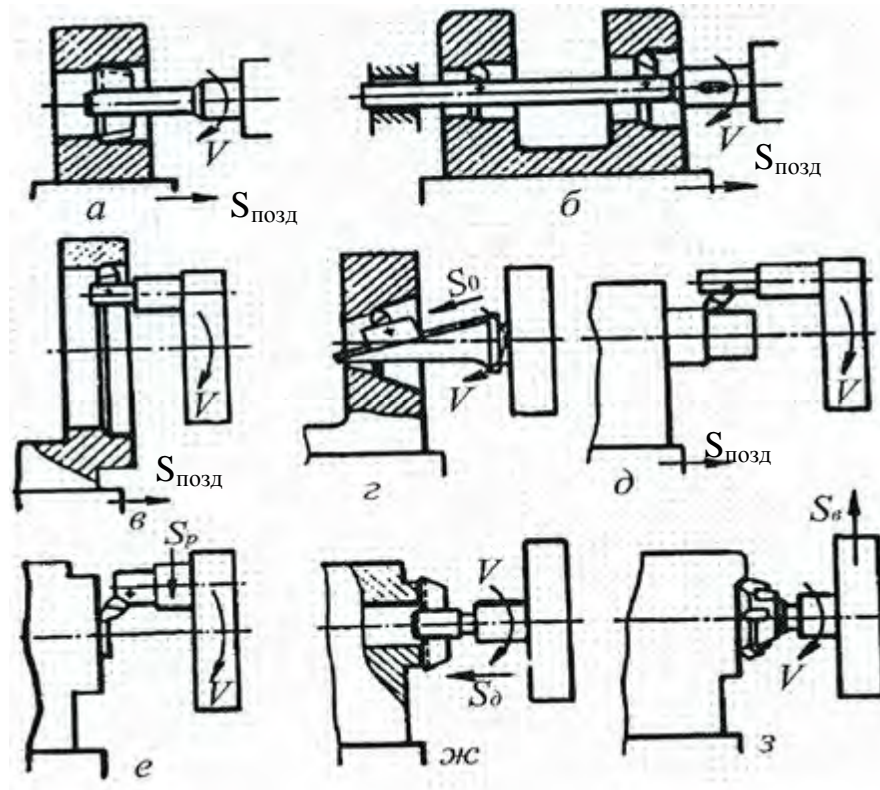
Схеми оброблення поверхонь заготовок на горизонтально-розточувальних верстатах
